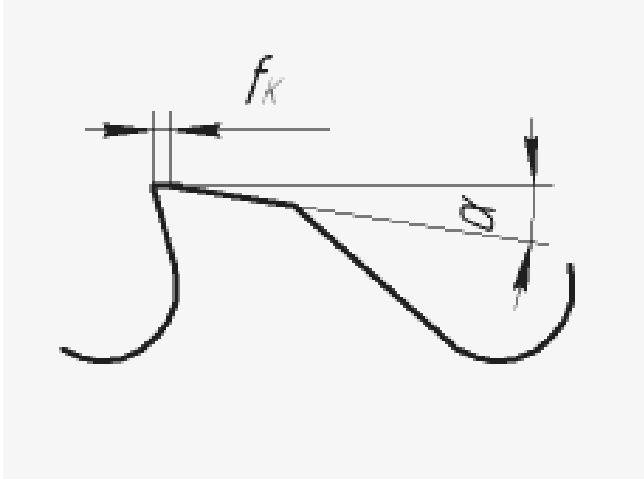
Размеры ленточки на калибрующих зубьях.
